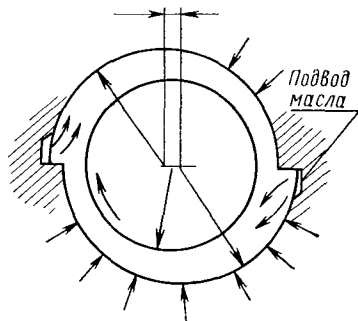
Схема установки вкладышей опорного подшипника ГТУ фирмы СТАЛ
